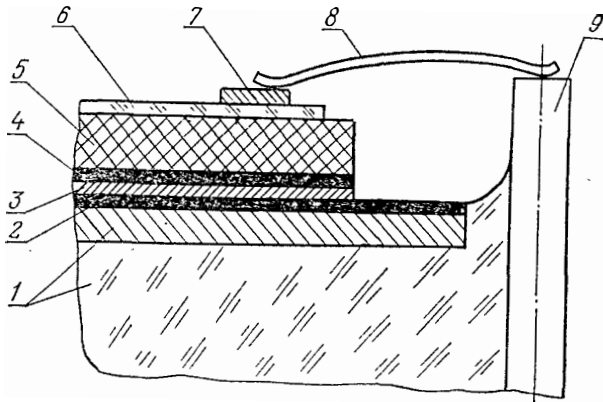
Крепление кристалла полупроводниковой ИМС к основанию корпуса: 1 — основание корпуса; 2 — сплав AuGe; 3 — слой золота; 4 — сплав AuSi; 5 — кристалл; 6 — окисная пленка; 7 — контактная площадка; 8 — проволочный вывод; 9 — вывод корпуса.
